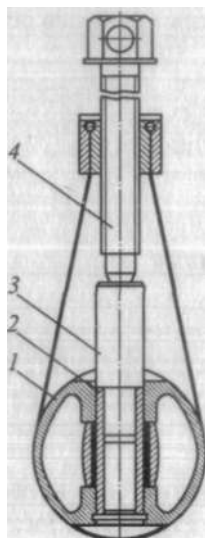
Приспособление для выпрессовки и запрессовки поршневого пальца: 1 - поршень; 2 - палец; 3 - оправка; 4 - винт
